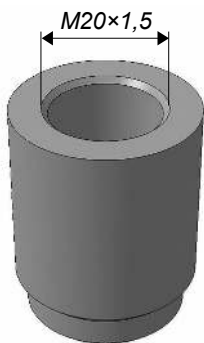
Вварная бобышка для крепежа преобразователя с помощью штуцера
